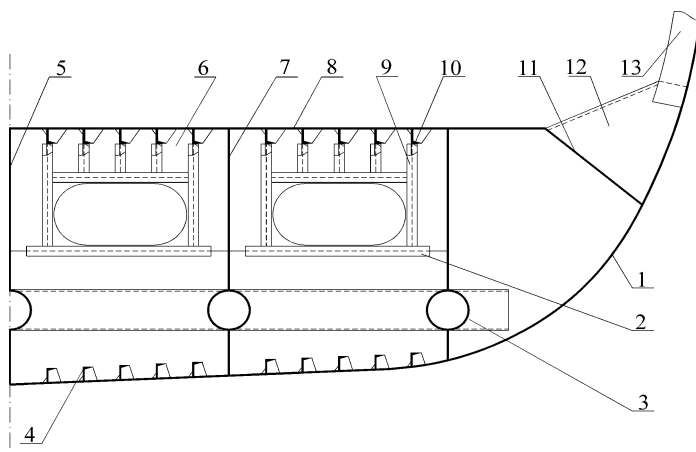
Схема днищевой конструкции с трубчатыми элементами конструктивной защиты
